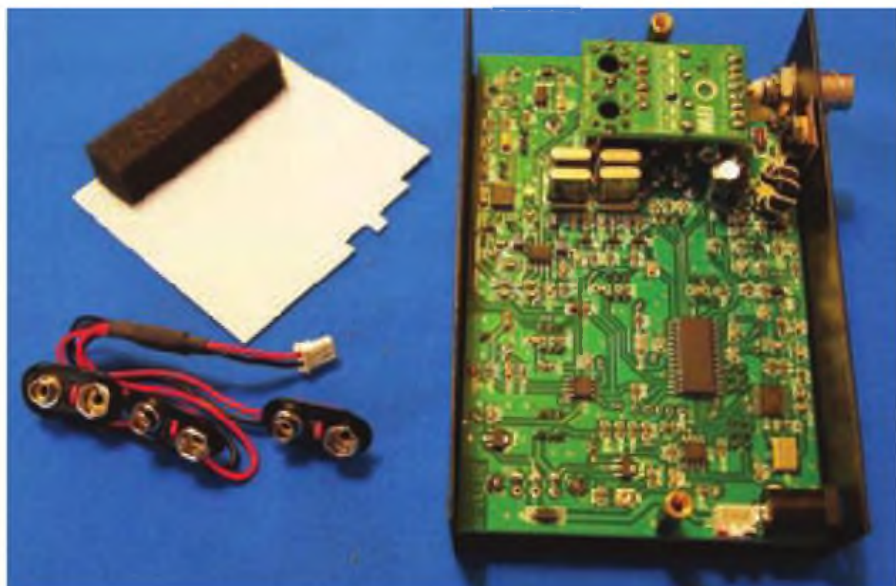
Foto B: El continente y los conectores para las pilas antes de ser instalado.
